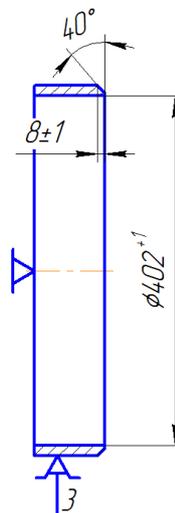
Эскиз базирования заготовки на 005 токарной операции.
